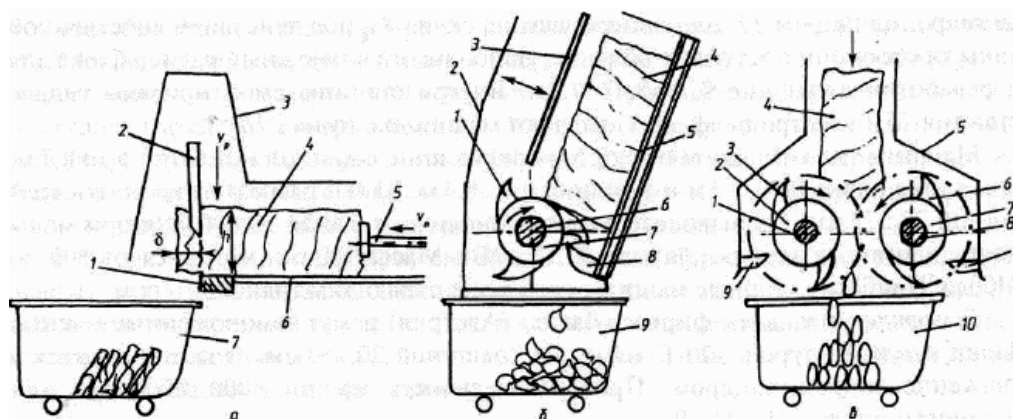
Схемы режущих механизмов блокорежек:
